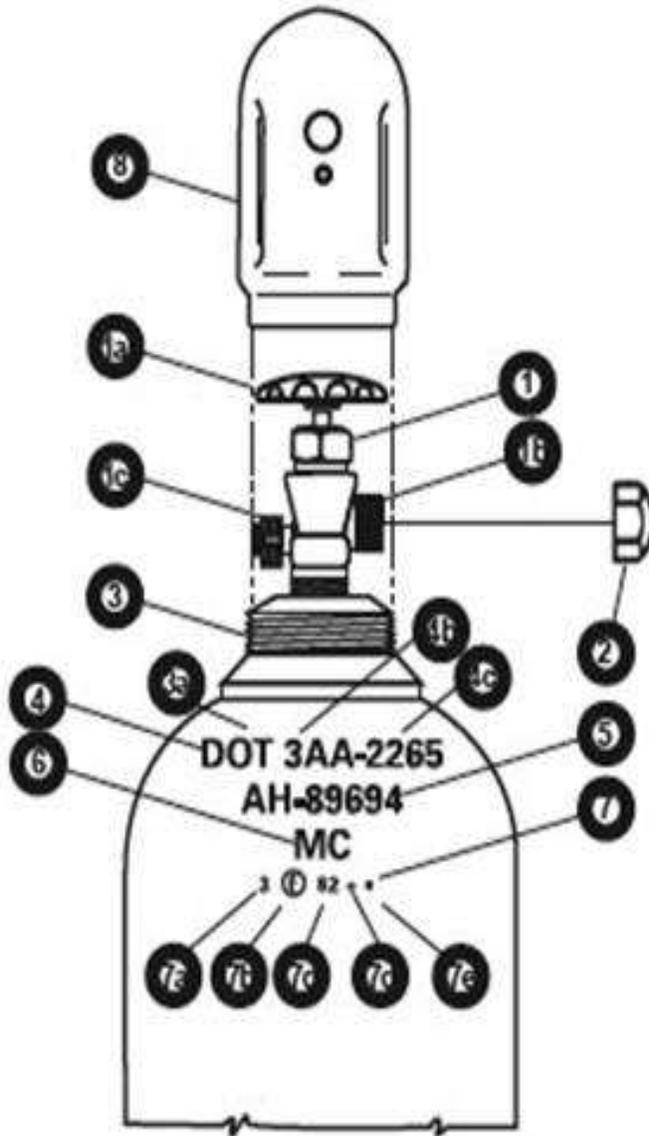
B- Partes que Integran el Manifold.
